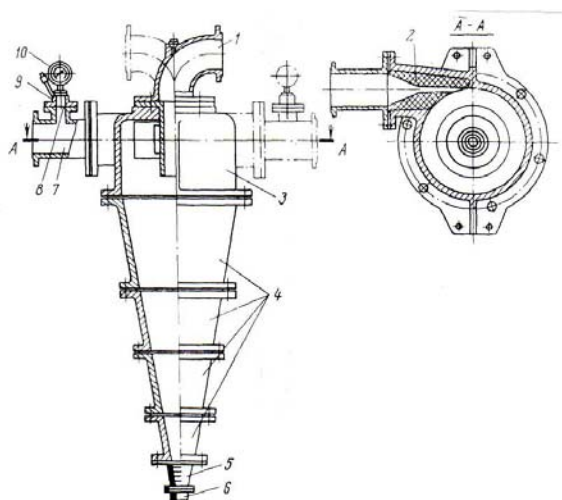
Классифицирующий конический гидроциклон: 1 – сливной патрубок; 2 – сменные вкладыши; 3 – цилиндр; 4 – конусы; 5 – конус из колец; 6 – песковая насадка; 7 – питательный патрубок; 8 – резиновая диаграмма; 9 – разделительная камера; 10 – манометр
